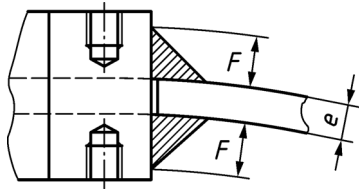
Typische Ausführungen von aufgeschweißten Anbauteilen
